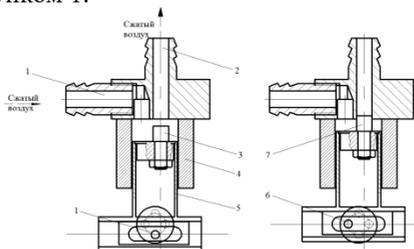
Устройство для прерывистой подачи сжатого воздуха
